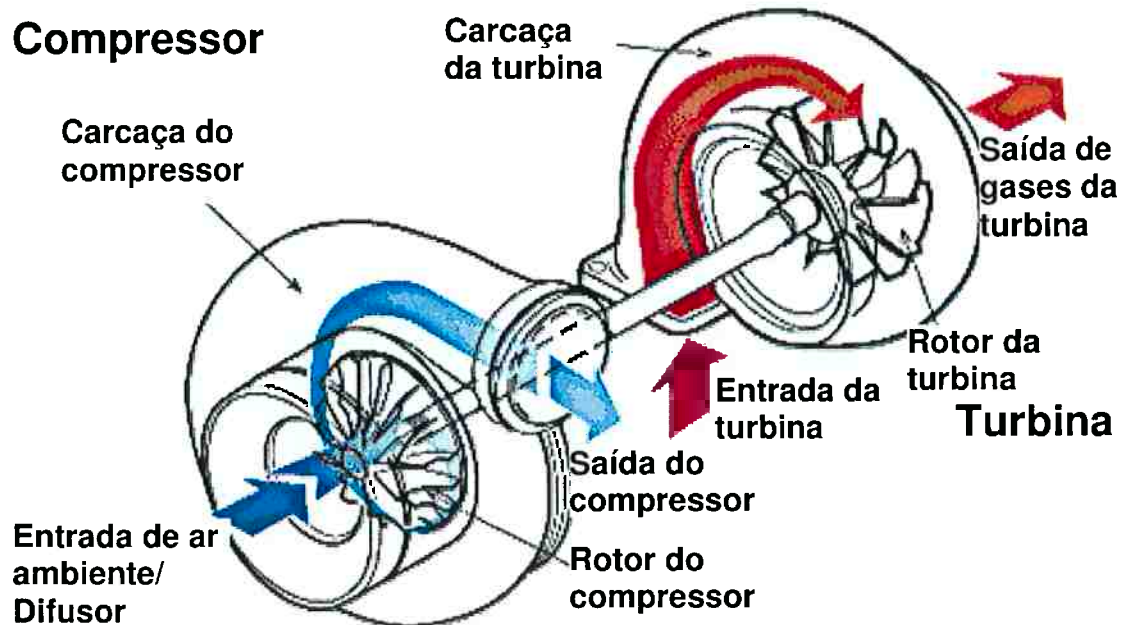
Fluxo no turbocompressor (GARRETT, 2004)
